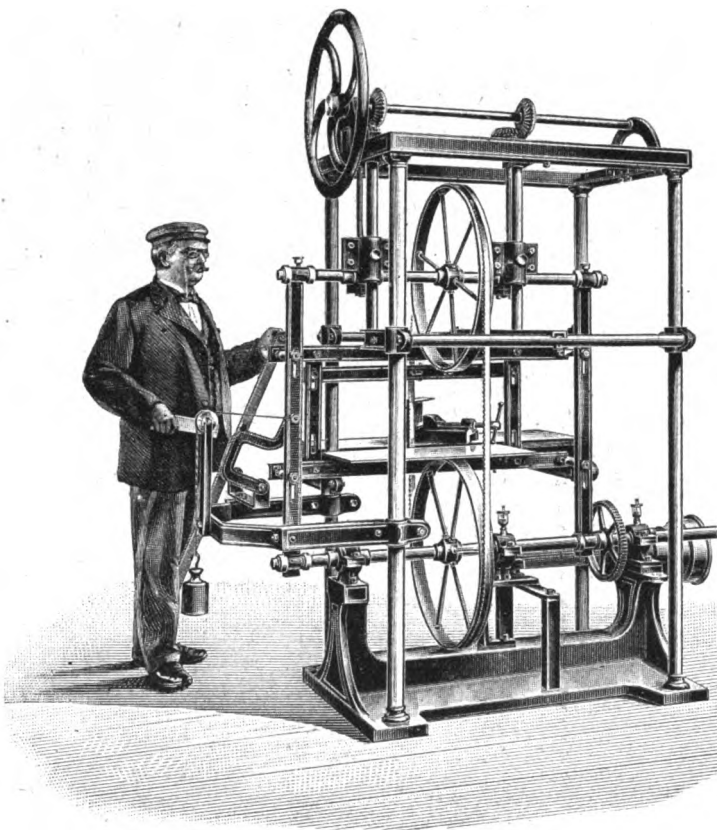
Metallbandsäge von der Fuldaer Maschinen- und Werkzeugfabrik Wilh. Hartmann in Fulda.
